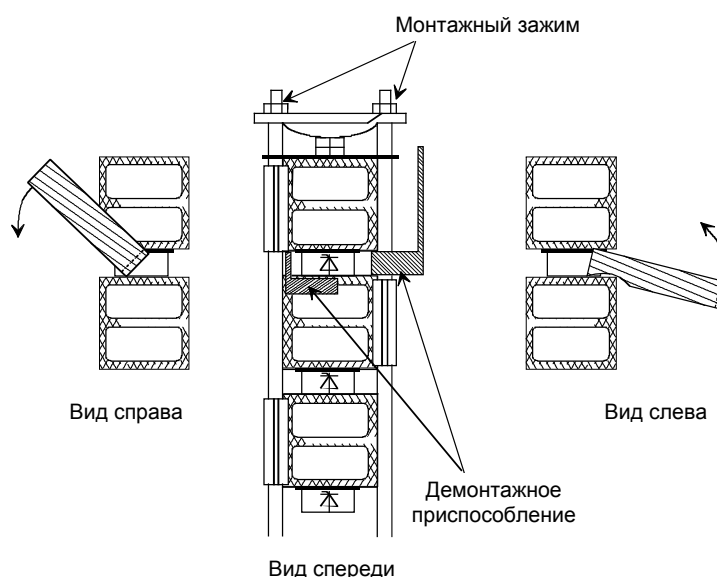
Как использовать демонтажное приспособление (на левом тиристорном блоке преобразователя)
